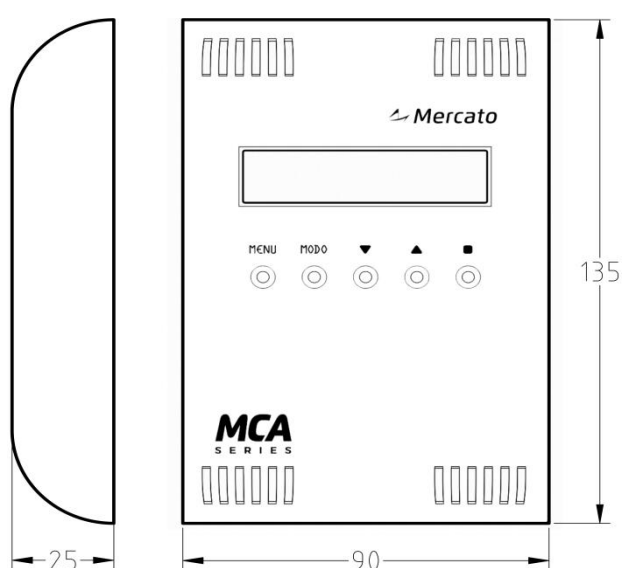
Dimensões da face do produto, em milímetros (mm).
